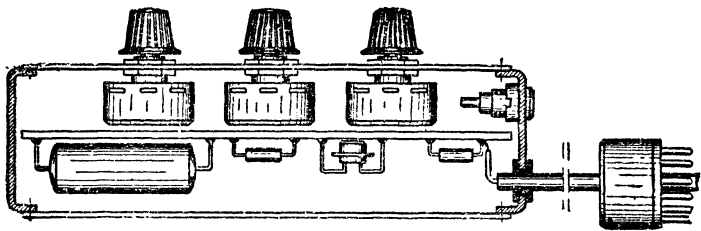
Внешний вид и размещение деталей в корпусе усилителя
